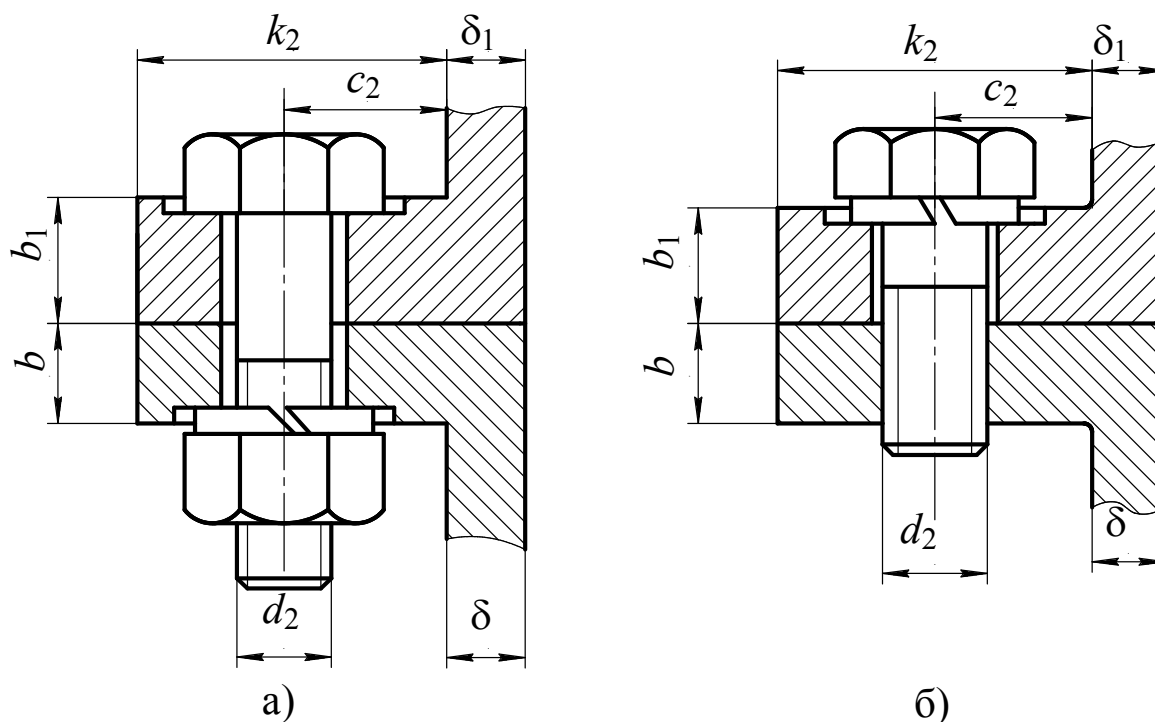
Размеры фланцев основания и крышки: а – крепление болтами; б – крепление винтами
